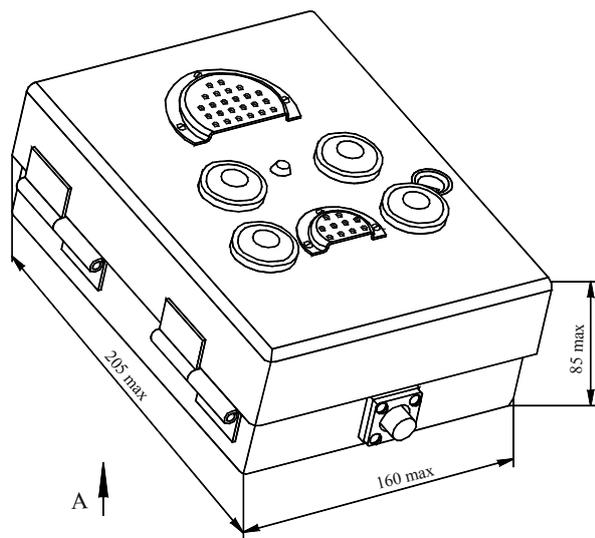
Внешний вид и габаритные размеры ПУ
